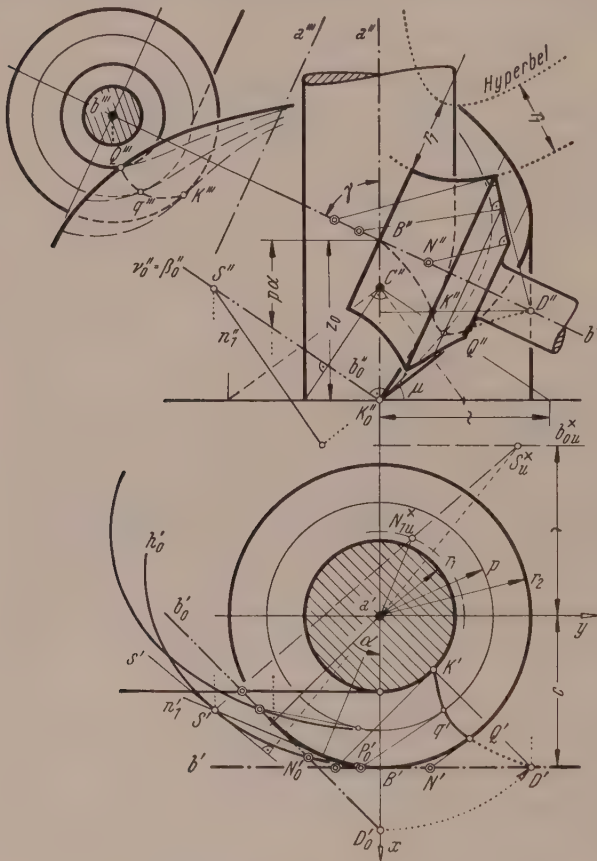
Scheibenfräser für Flachgewindeflanken.
